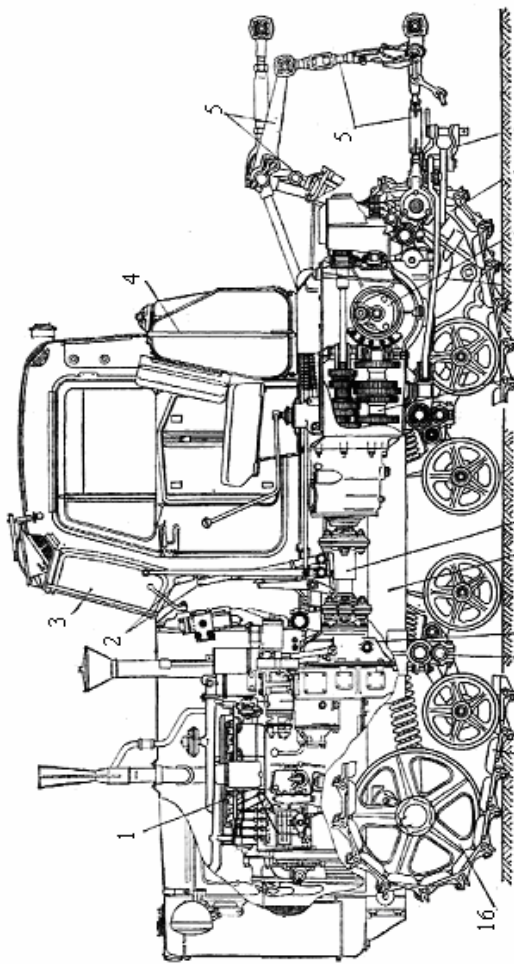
Розміщення основних частин, їх механізмів й деталей гусеничного трактора ДТ-75М
